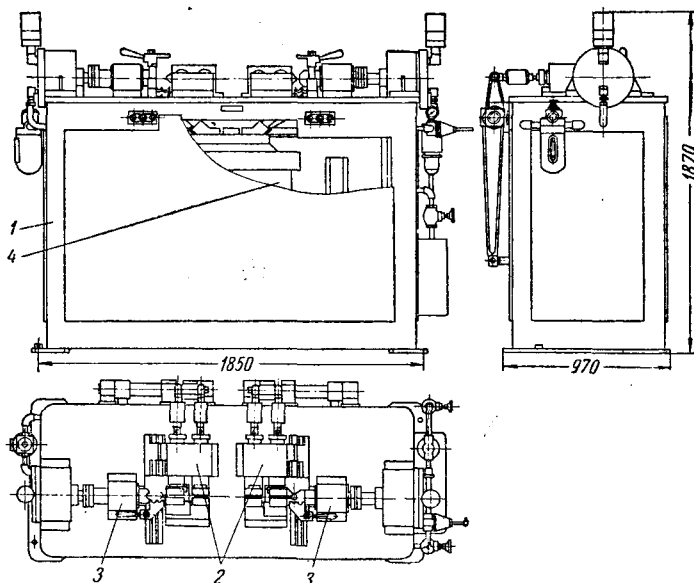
Общий вид конденсаторной машины для сварки соединений основания остова с распорными трубами.
